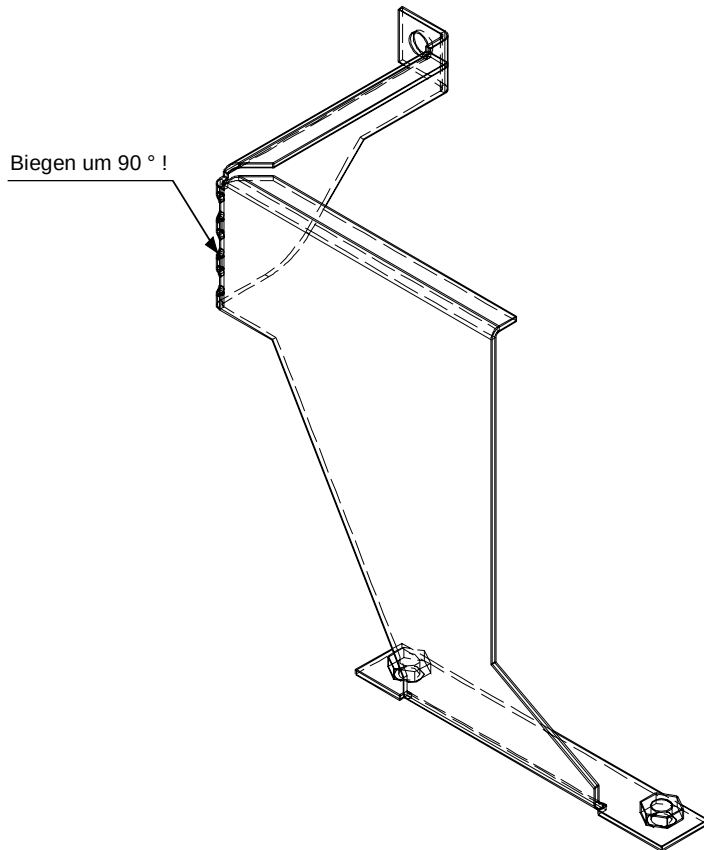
Endzustand des Haltebleches für die SSB-Baugruppe
